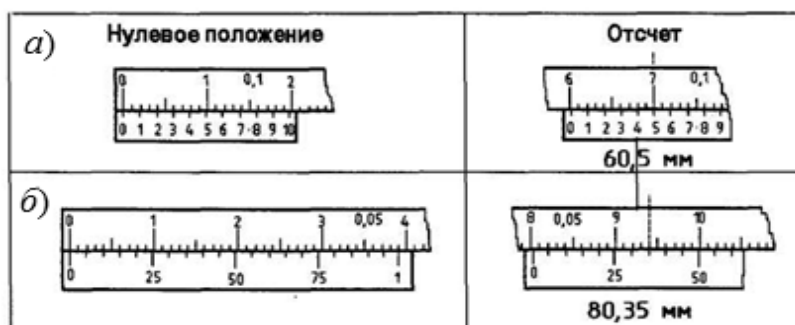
Пример отсчета показаний штангенциркуля
